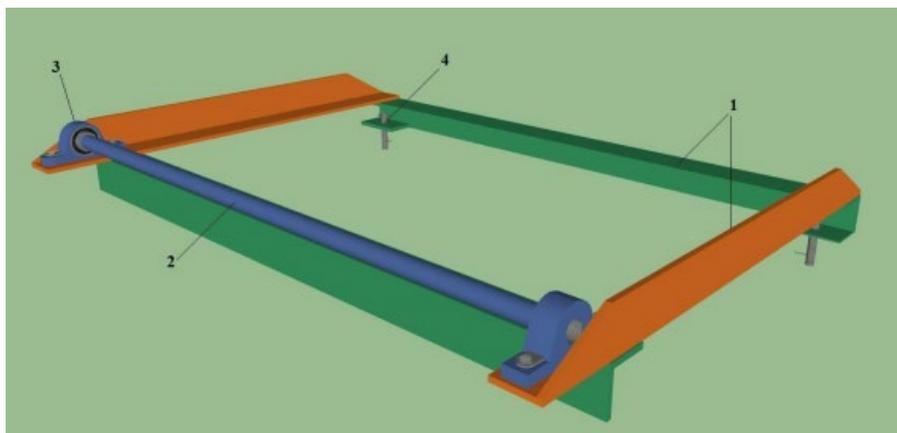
Устройство конструкции: 1 – металлический уголок (63х63х4); 2 – металлическая труба диаметром 32 мм.; 3 – корпусный подшипник типа UCP207; 4 – струбцина для крепления к подоконнику.
